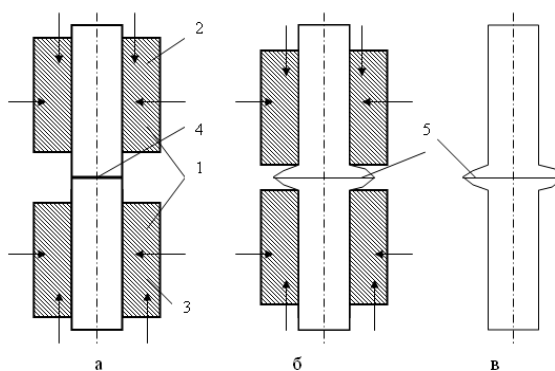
Схема холодной стыковой сварки: 1 – зажимы; 2, 3 – концы заготовок; 4 – место стыка; 5 – грат (облой); а – зажим заготовок; б – сдавливание с образованием грата; в – соединенные заготовки с гратом; стрелки показывают направление действия сил на инструмент
